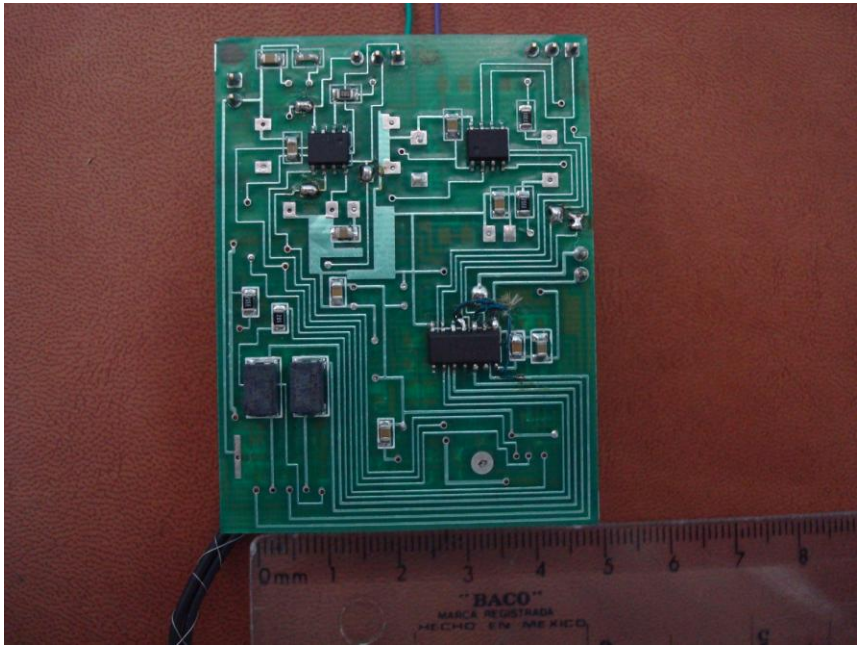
Fotografía de la unidad electrónica de la espalda de la rata (lado soldaduras).
